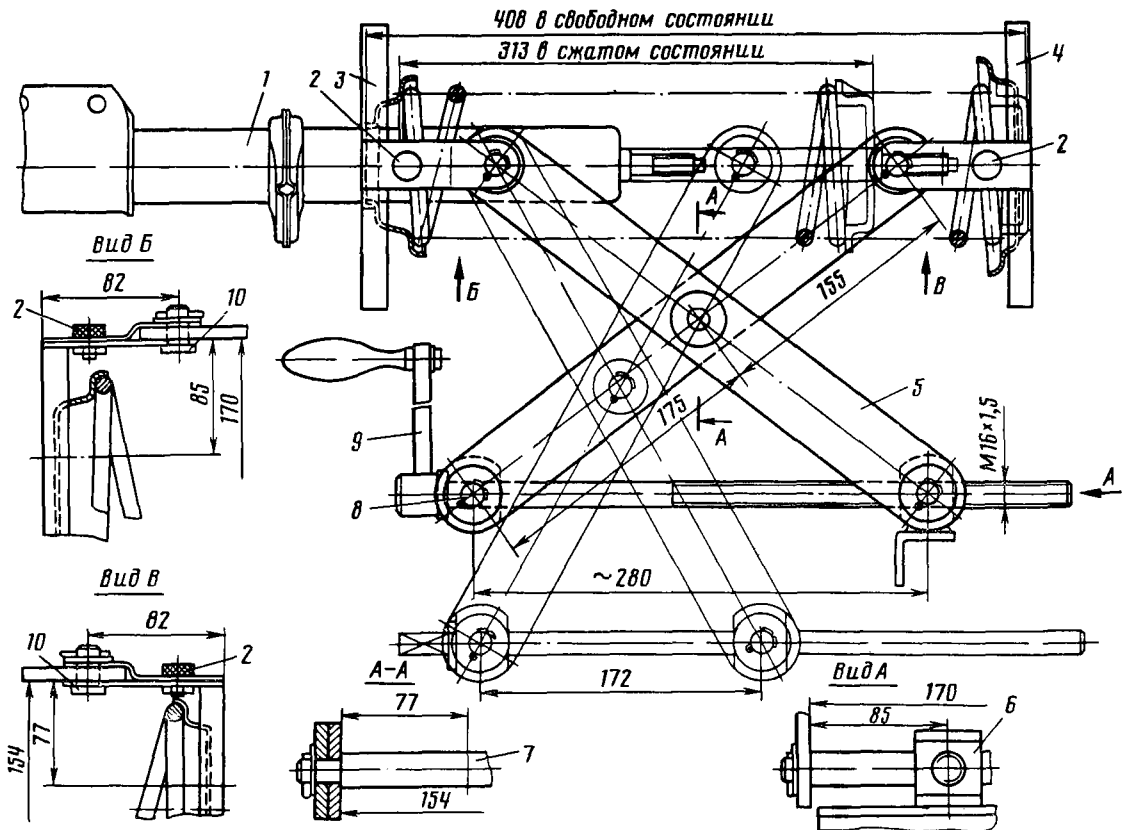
Приспособление для сборки и разборки пружины со стойкой передней подвески (вариант 1):
